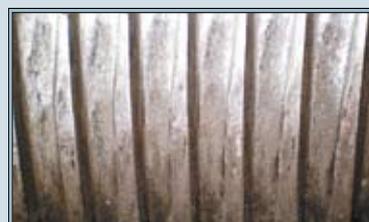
Неравномерный износ зубьев зубчатой муфты при несоосности валов
